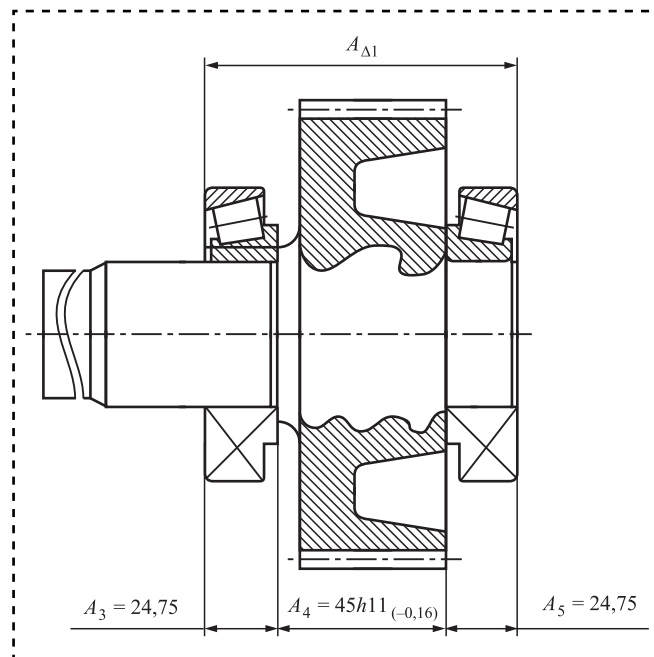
Вал—колесо редуктора с напрессованными подшипниками
